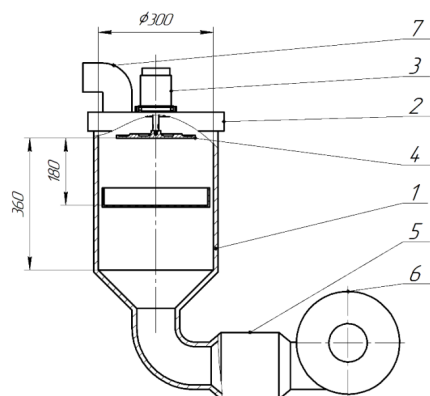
Структурная схема ультразвуковой лабораторной сушильной установки: 1 – корпус сушильной установки; 2 – крышка сушильной установки; 3 – корпус дискового излучателя; 4 – дисковый излучатель; 5 – труба подвода нагретого воздуха; 6 – вентилятор; 7 – труба отвода воздуха
